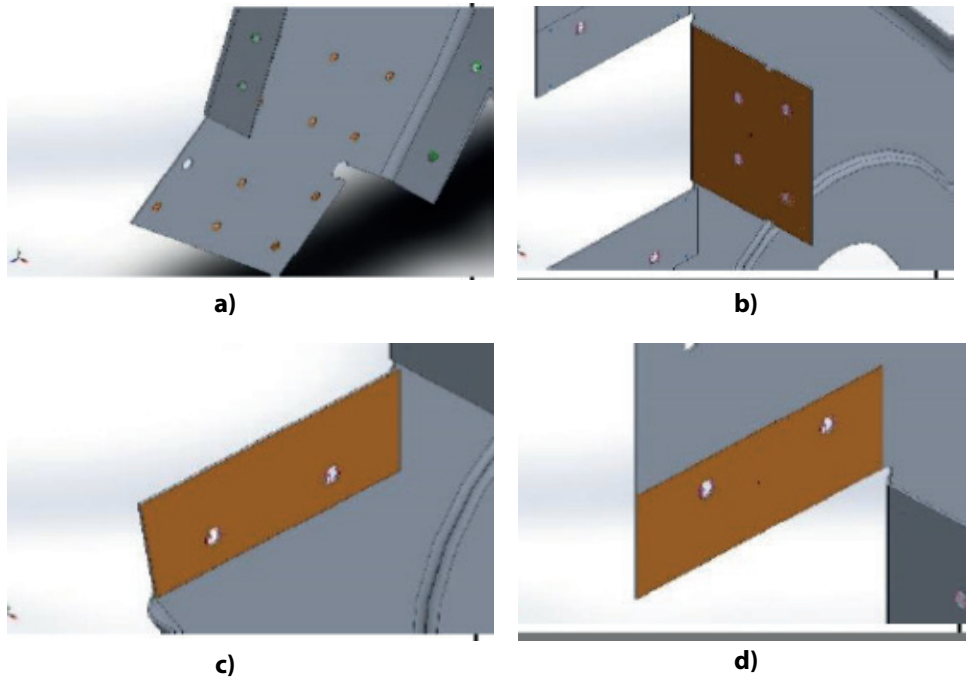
Sujeciones del lado A de la cuaderna: a) conexión fija, b) conexión de cara plana con viga principal, c) y d) conexión de cara plana con largueros
